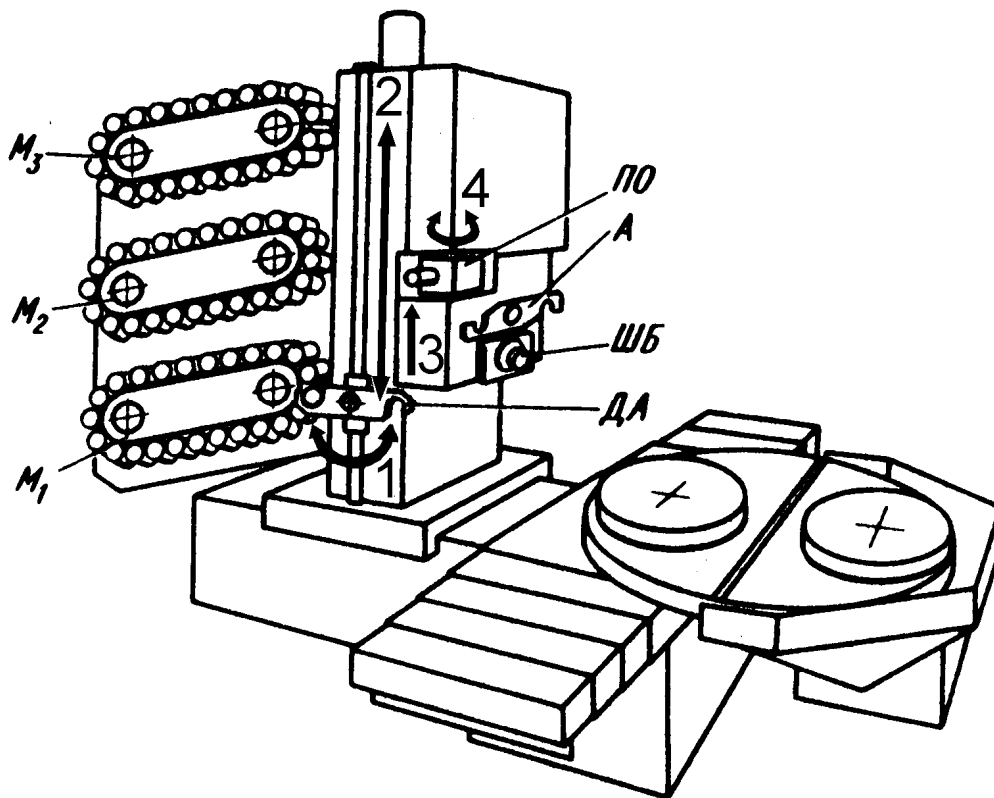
Пристрій А3І для БВ з трьома змінними магазинами
